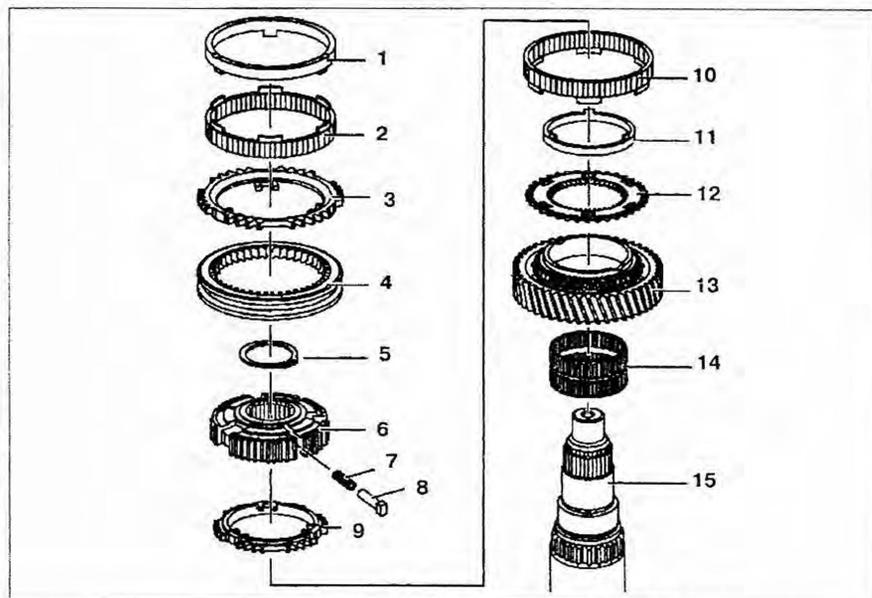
Снятие и установка шестерни 3-й передачи:
